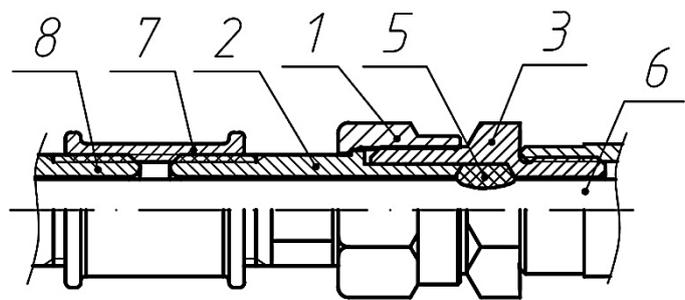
Кабельный ввод для прокладки кабеля в трубе Т10 и Т14 с проложенным кабелем в трубе
